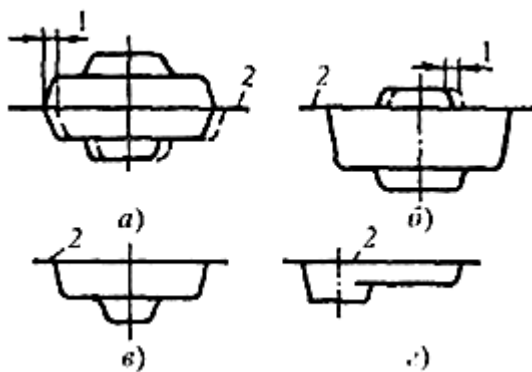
Положение поверхности разъёма: а- правильное; б - неправильное; в - смещенное для плоской круглой заготовки; г – смещенное для плоской удлиненной в плане заготовки; 1 – смещение половин штампа; 2 –
